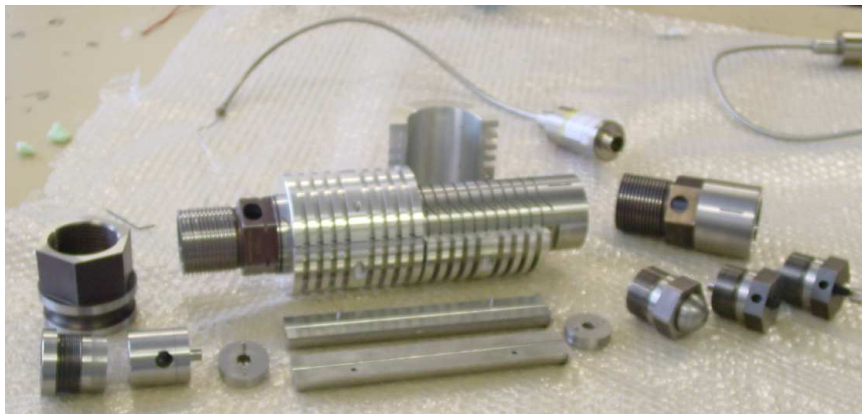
Vue d'ensemble des éléments de la buse instrumentée
